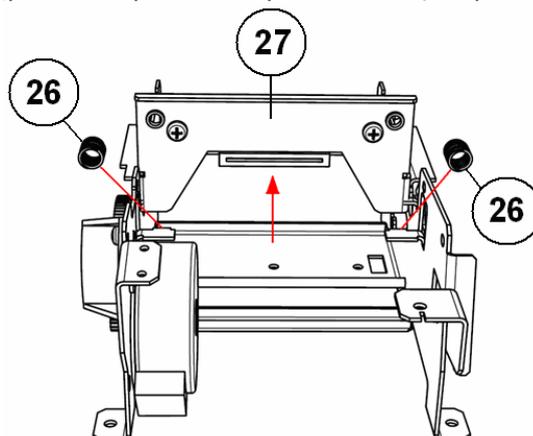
Печатающая головка вынута из пазов узла печати
